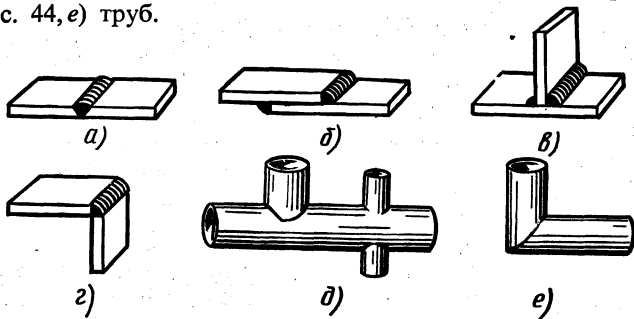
Сварные соединения деталей (а...г) и труб (д, е): а — стыковое, б — нахлесточное, в, д — тавровое, г, е — угловое
